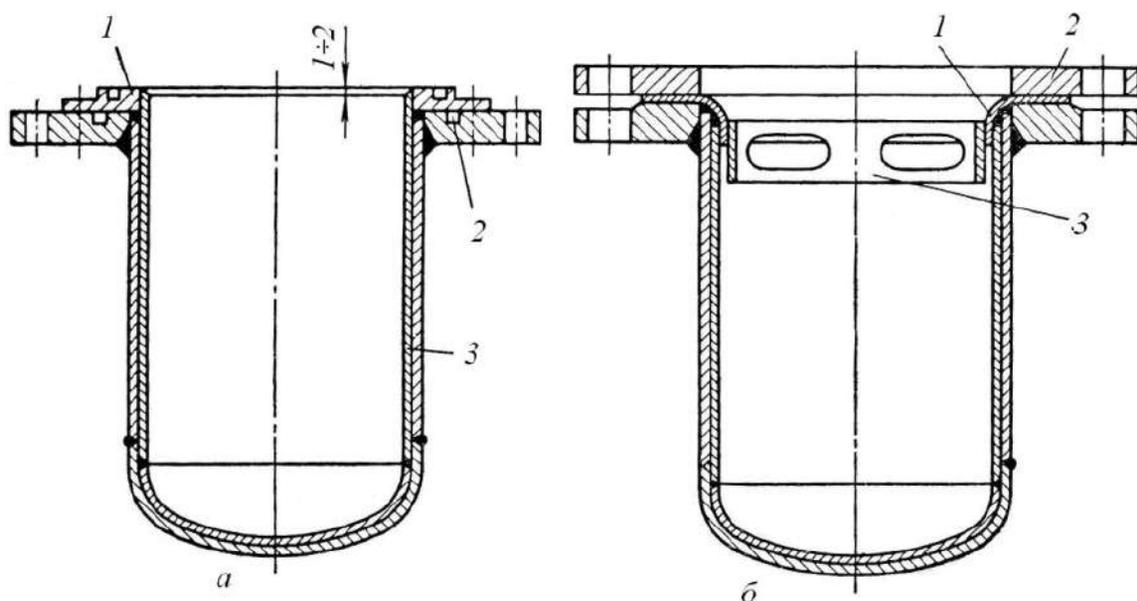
Корпус аппарата с футеровкой из листового титана, выполненной способом «вставного вкладыша» со сваркой титановой обечайки с титановым днищем встык:
